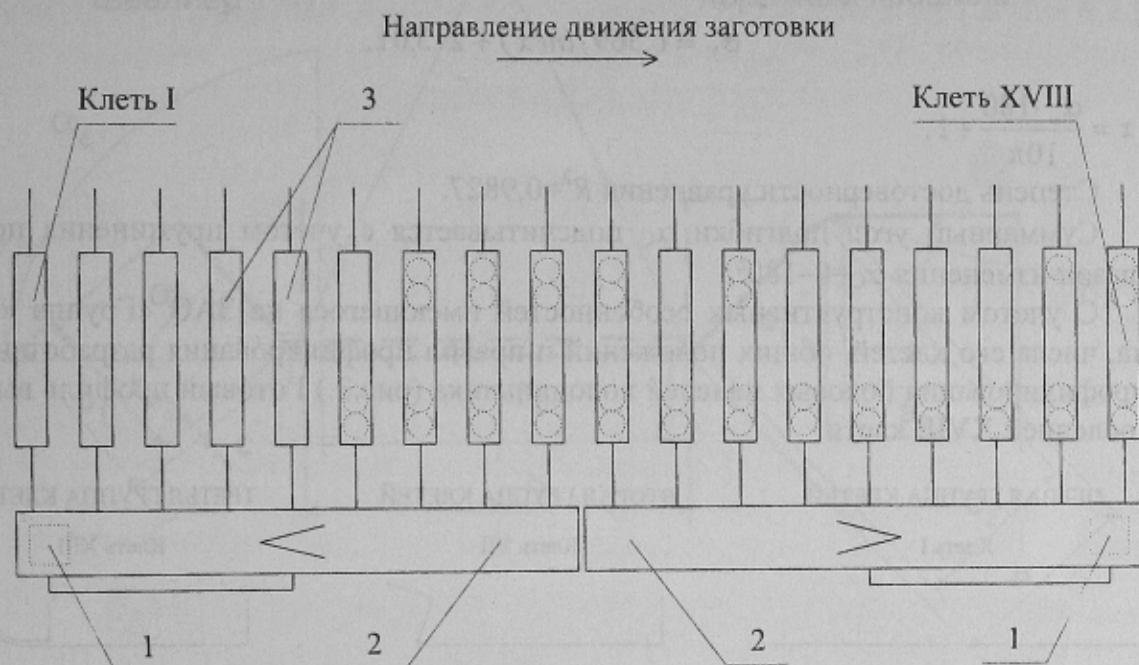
План расположения оборудования восемнадцатиклетевого профилигибочного стана для изготовления боковых панелей бытовых холодильников: 1 — двигатели; 2 — шестеренные клетки; 3 — рабочие клетки с горизонтальными и вертикальными (показаны пунктиром) валками
